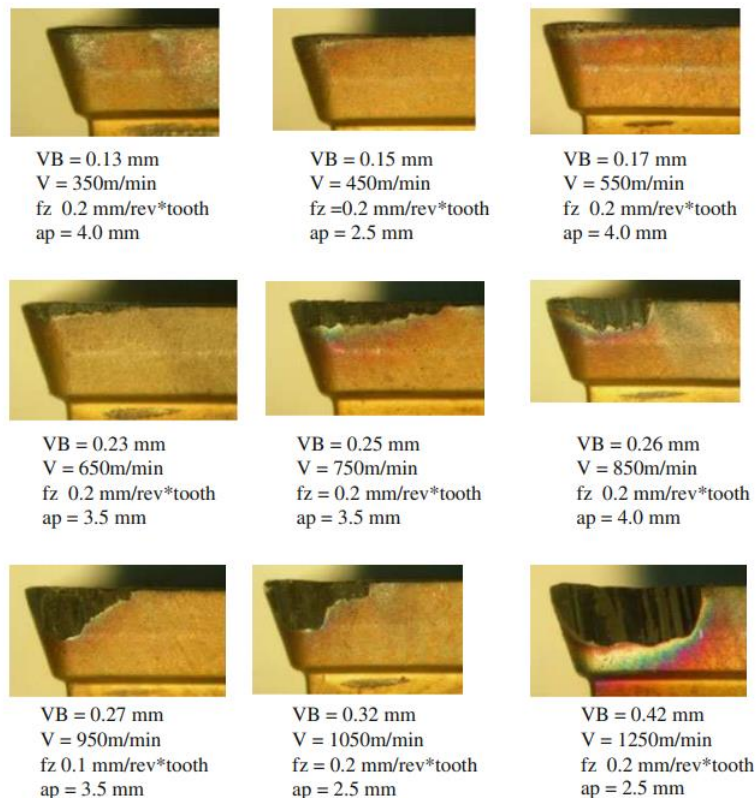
Зношування інструменту при торцевому фрезеруванні сталі AISI 1045 за різних умов різання
